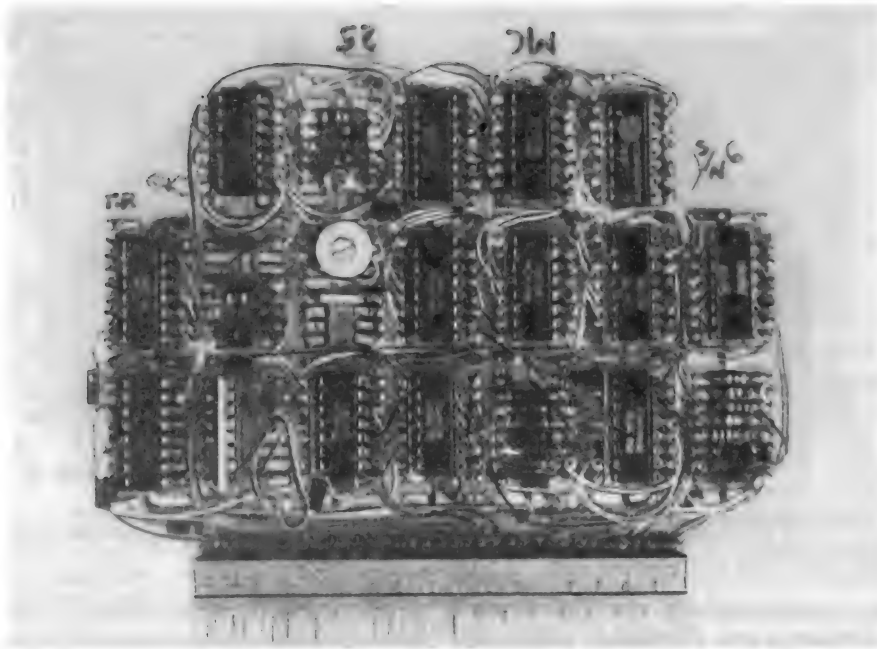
Платы с соединениями накруткой обеспечивают точный и быстрый монтаж, особенно они хороши для схем с цифровыми ИМС. Эта плата сделана по образцу печатной схемы, штырьки для соединения накруткой вынесены на компонентную сторону в отличие от обычного расположения штырьков на нижней стороне. Такая специфическая компоновка платы диктуется внутренними габаритами океанографического датчика давления, для которого она предназначена.
